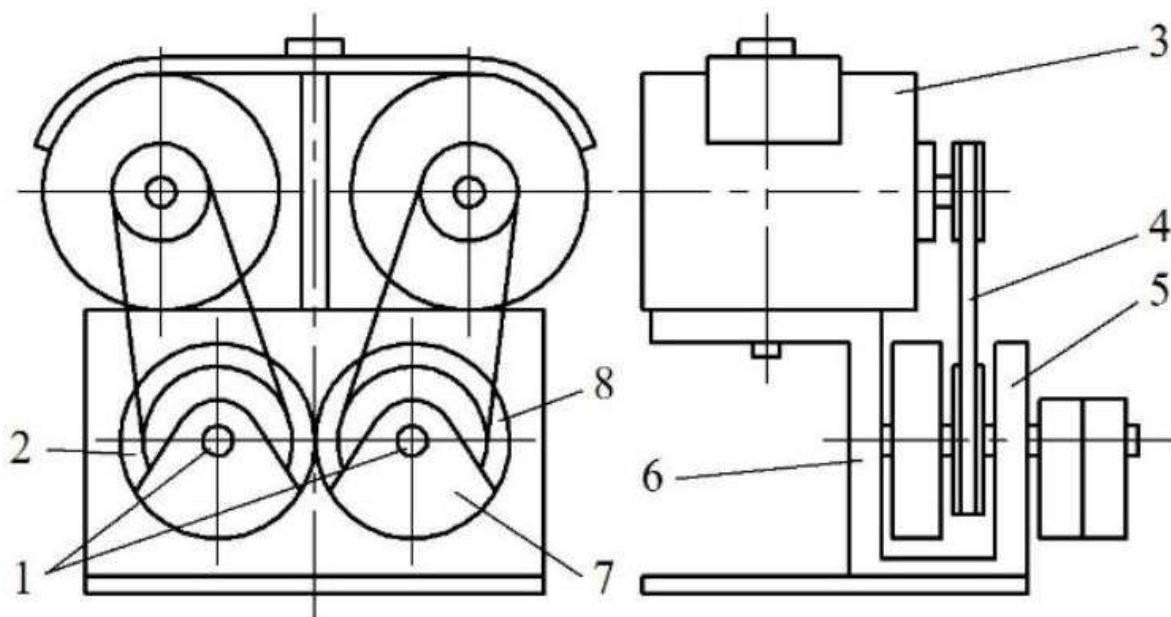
Схема электромеханического вибратора направленного действия: 1 – валы; 2 и 8 – зубчатые колеса; 3 – микроэлектродвигатель; 4 – клиноременная передача; 5 – основание; 6 – корпус; 7 – дисбалансы
